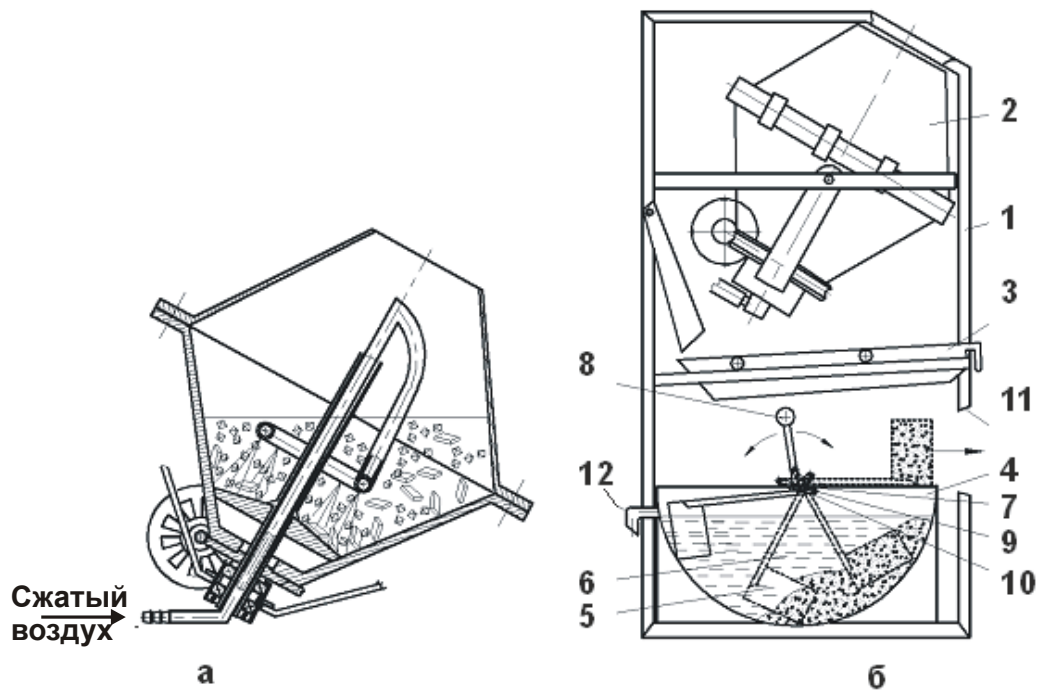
Компонировочная схема устройства для абразивной обработки затопленными струями: а – схема рабочей камеры; б – струйно-абразивная установка по А. с. №1664525 [22]
